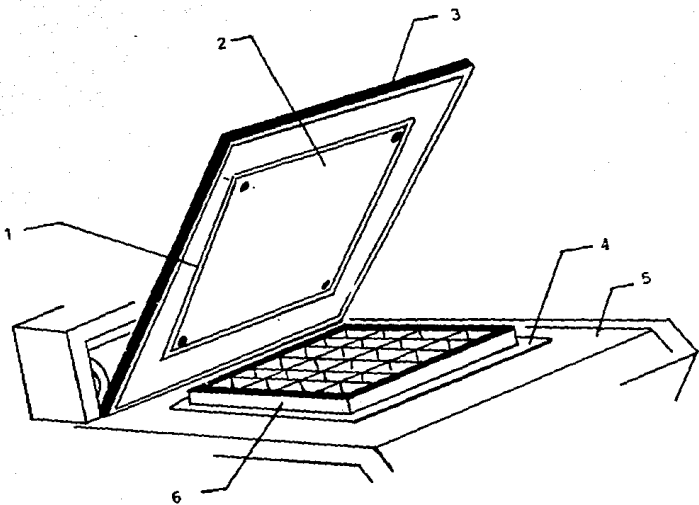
MONTAJE DEL SUAJE EN LA PLATINA FIJA. 1.- Papel
